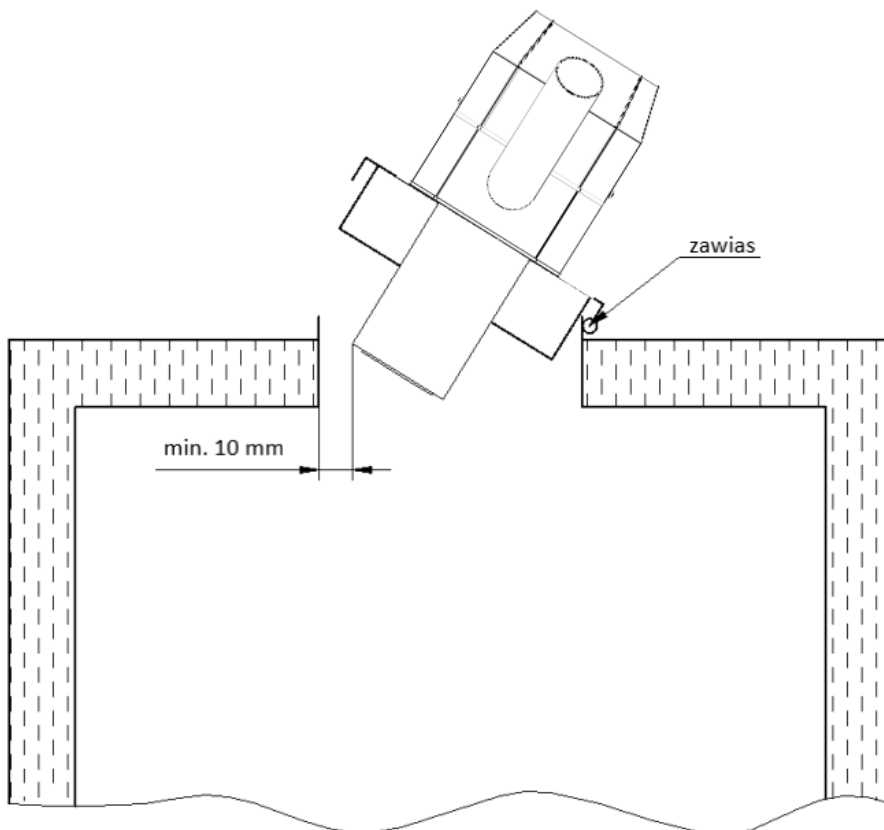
Пространство для установки горелки. Вид сверху.
